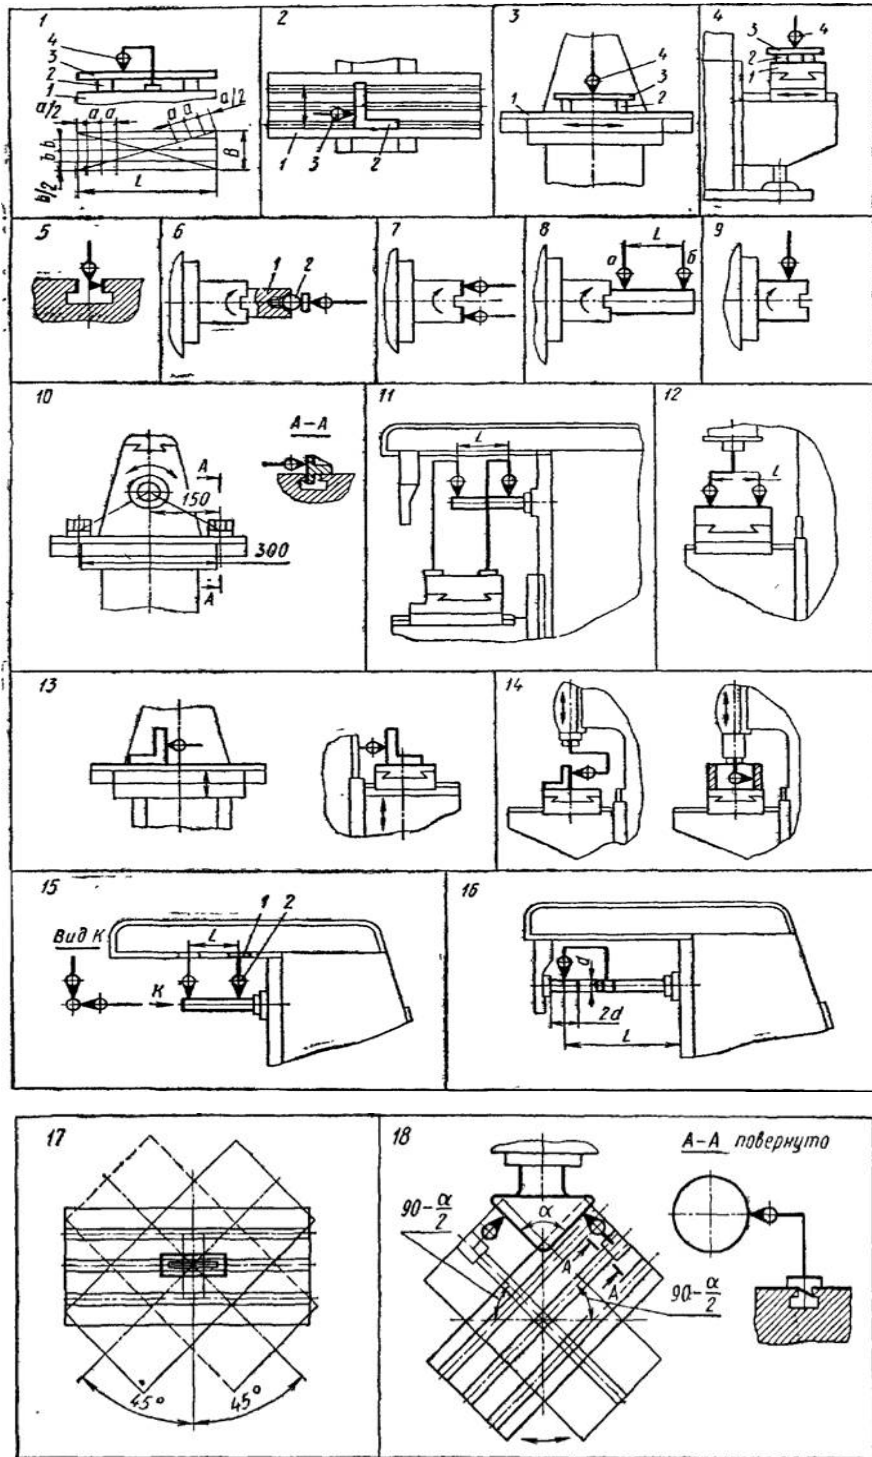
Схеми перевірок консольно-фрезерних верстатів на геометричну точність: 1-18 номера перевірок (ГОСТ 17734-72)
